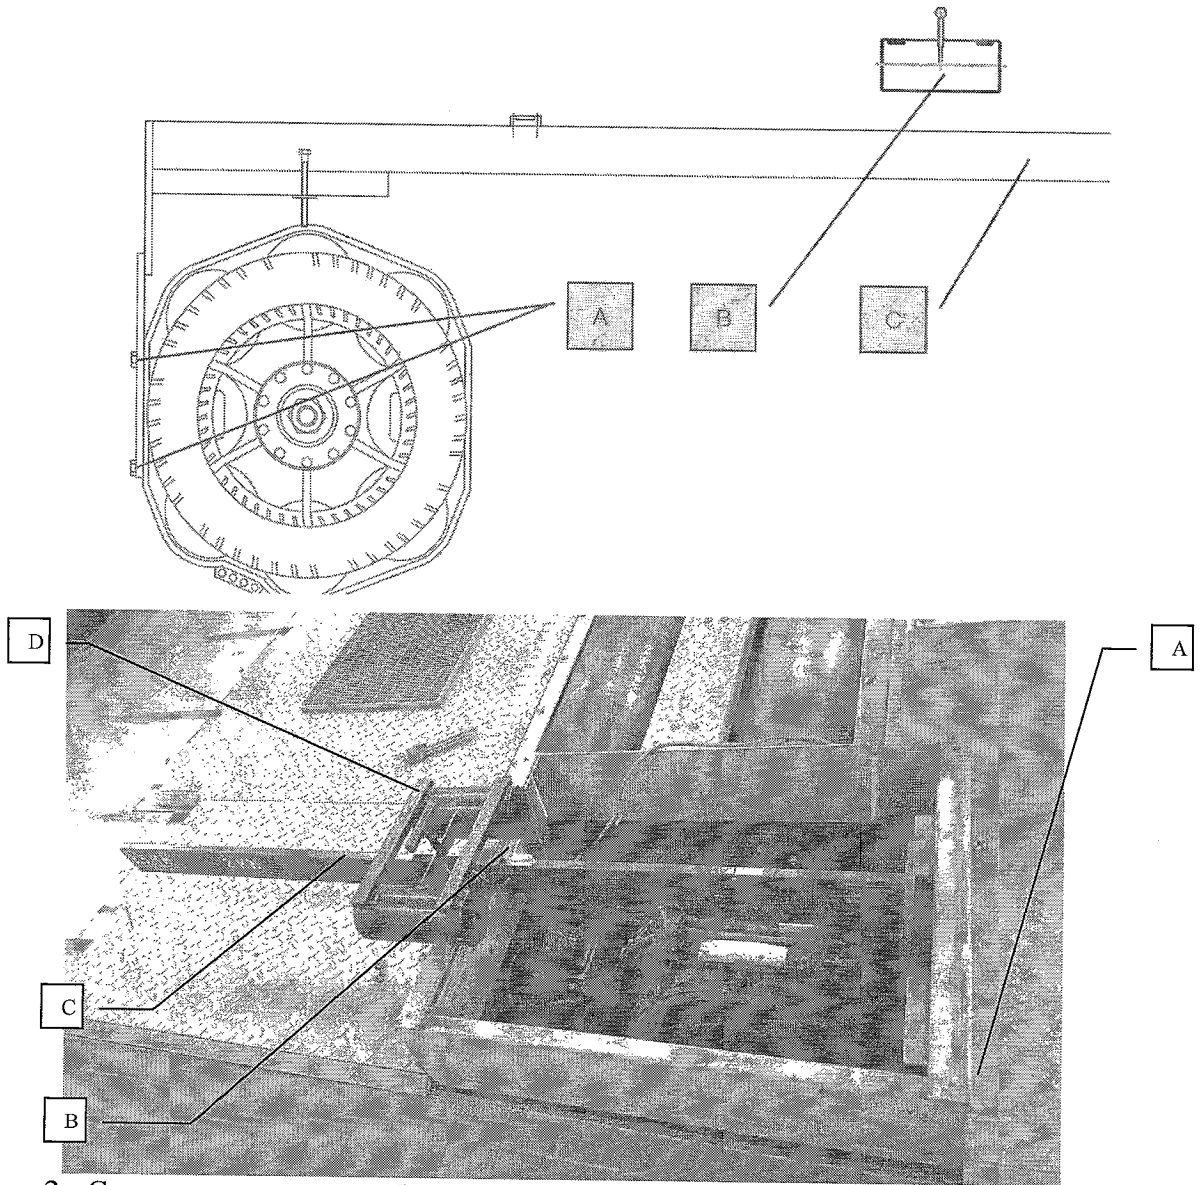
Схема установки калибровочного рычага для модификации LPS 3000, MSR 1000, MSR 1050. (А – монтажный кронштейн; В - калибровочный груз; С – калибровочный рычаг; D – пузырьковый уровень)
